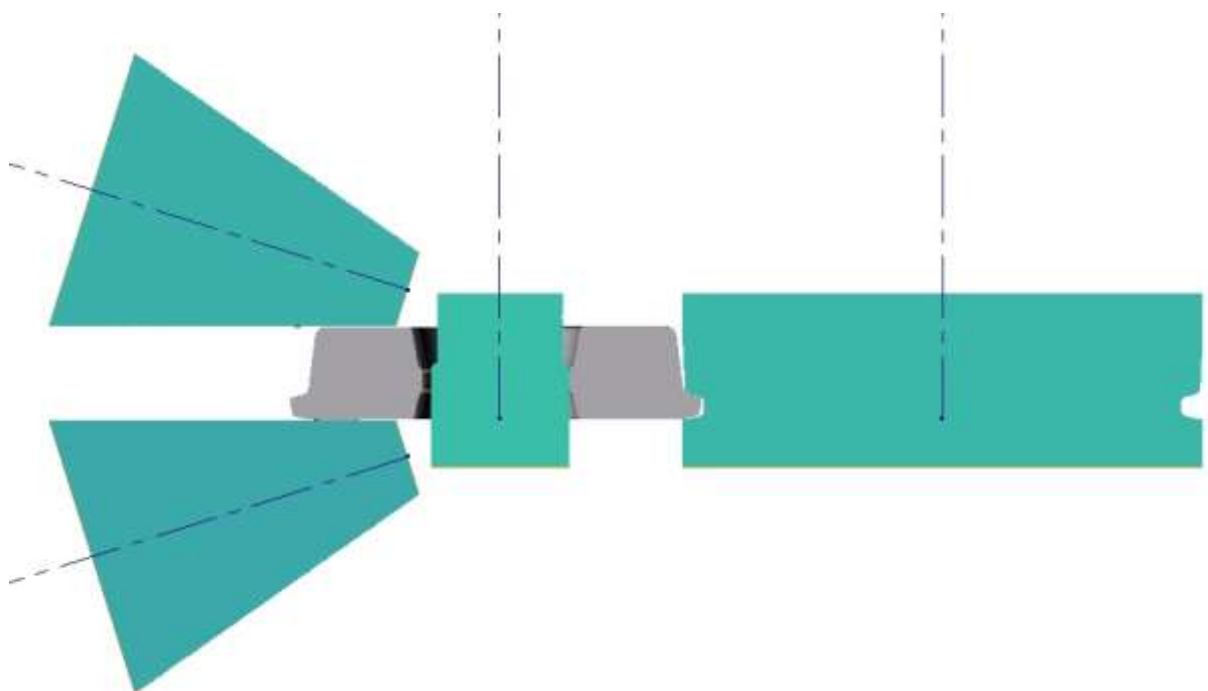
Расположение рабочего инструмента и заготовки в начале процесса раскатки
